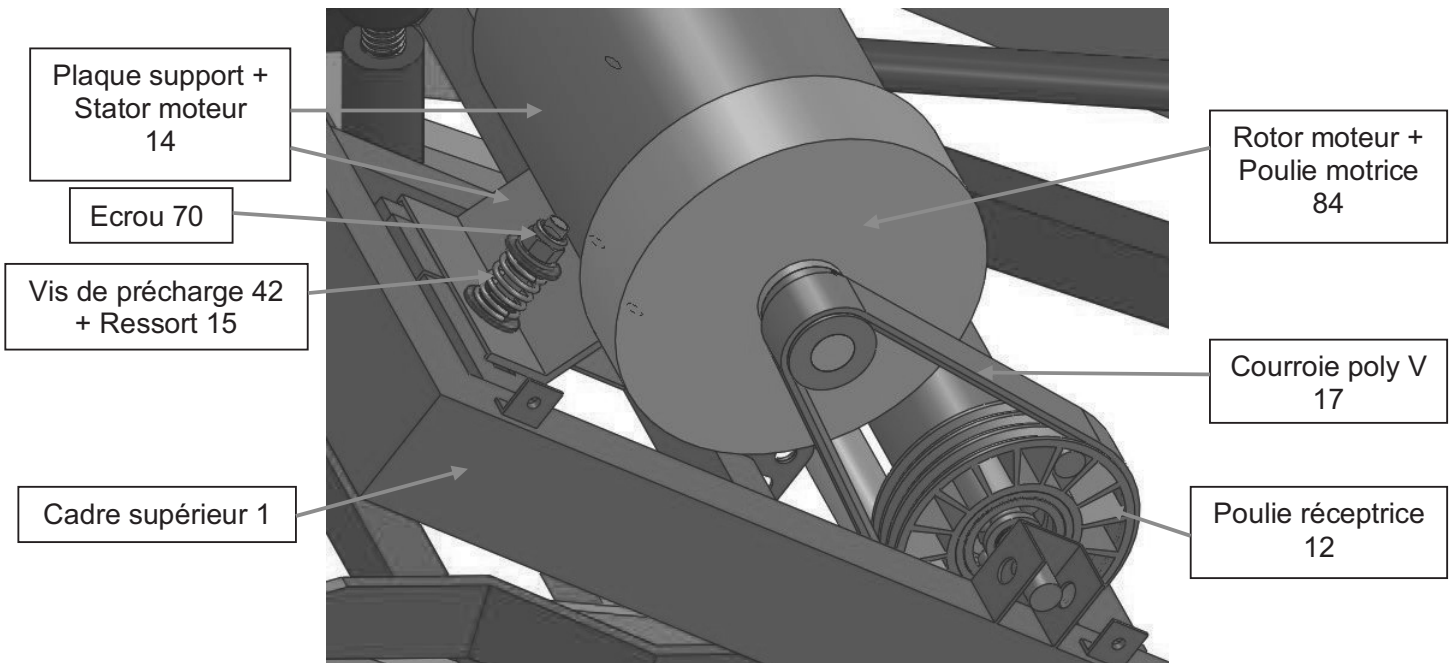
Vue d'ensemble du dispositif de tension de la courroie du moteur
